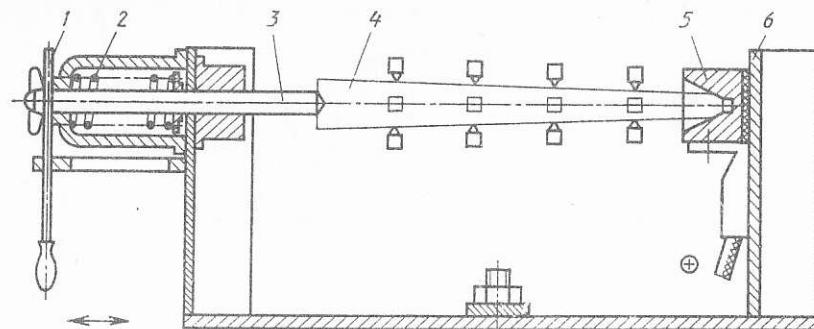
Приспособление с быстродействующим зажимом для отрезки литников
